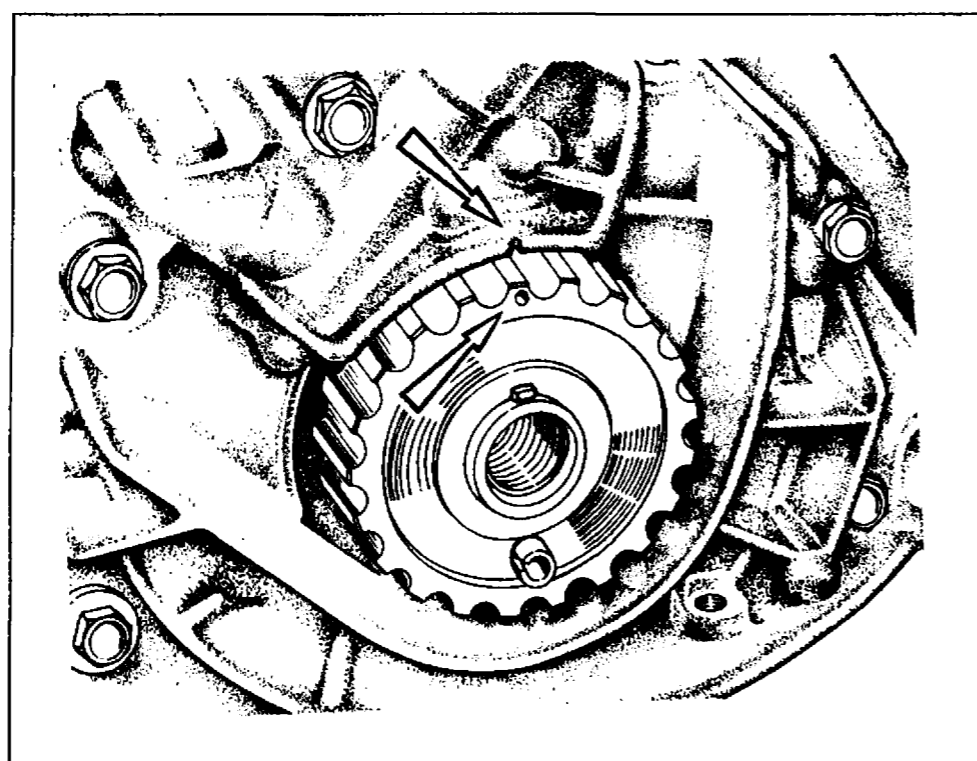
Проверка совпадения установочных меток на шкиве коленчатого вала и крышке масляного насоса
